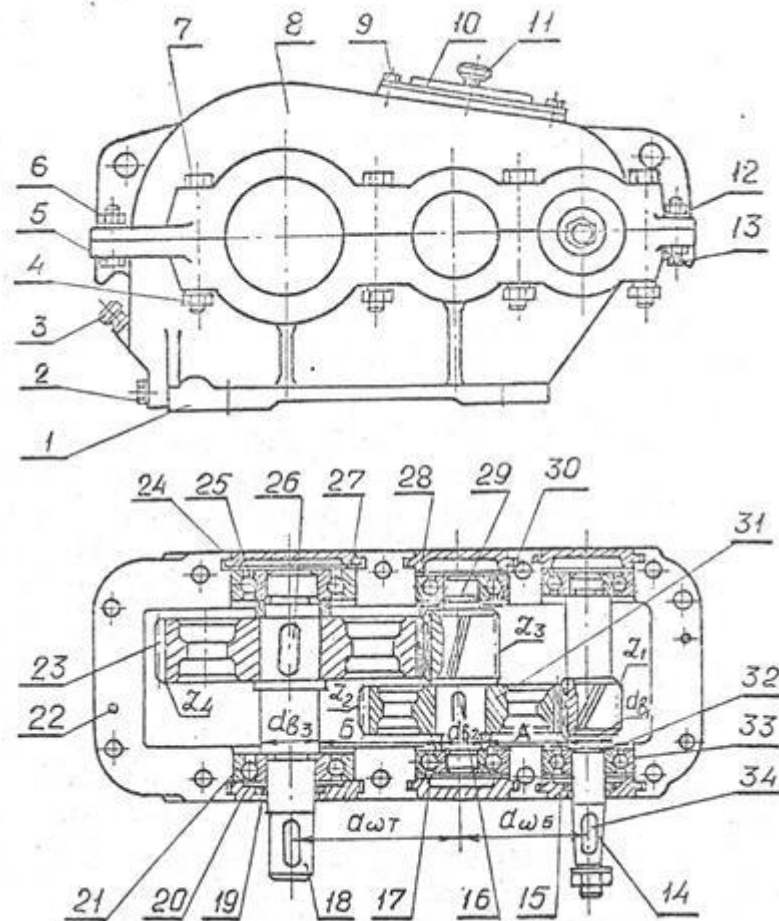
Двухступенчатый цилиндрический редуктор
